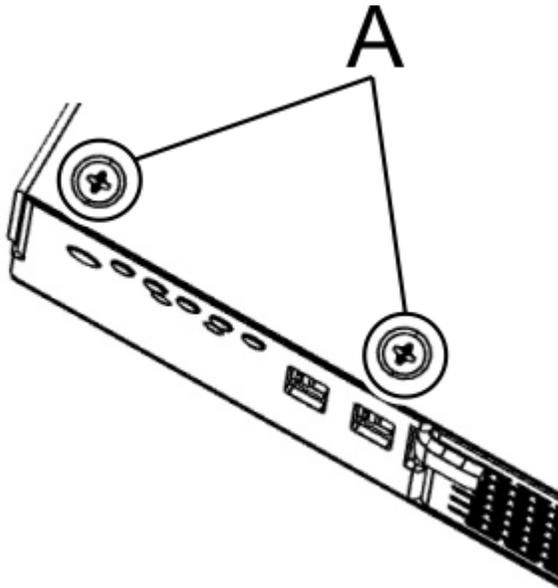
Schrauben an der Unterseite der Steuerkonsole entfernen
